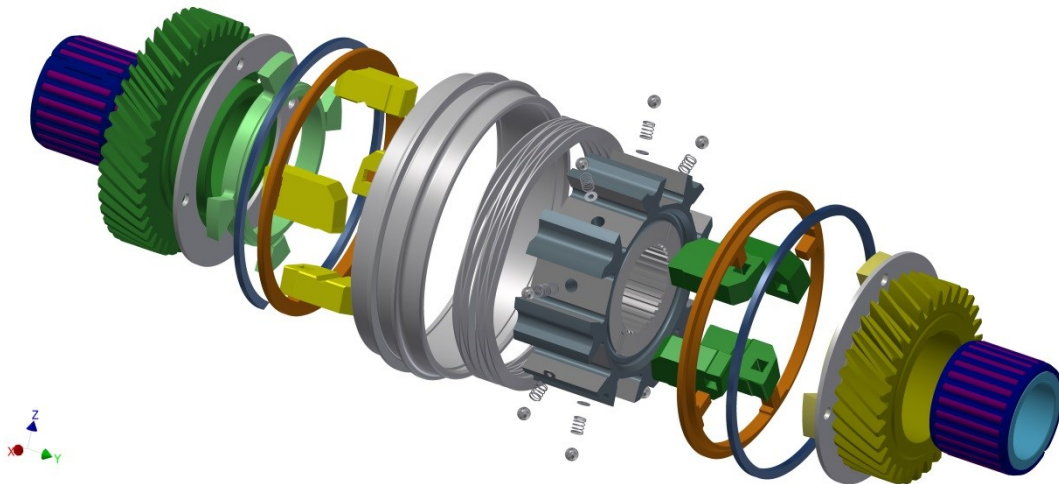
(Rozpad mechanismu pro testovací převodovku verze 1) [zdroj: autor]
